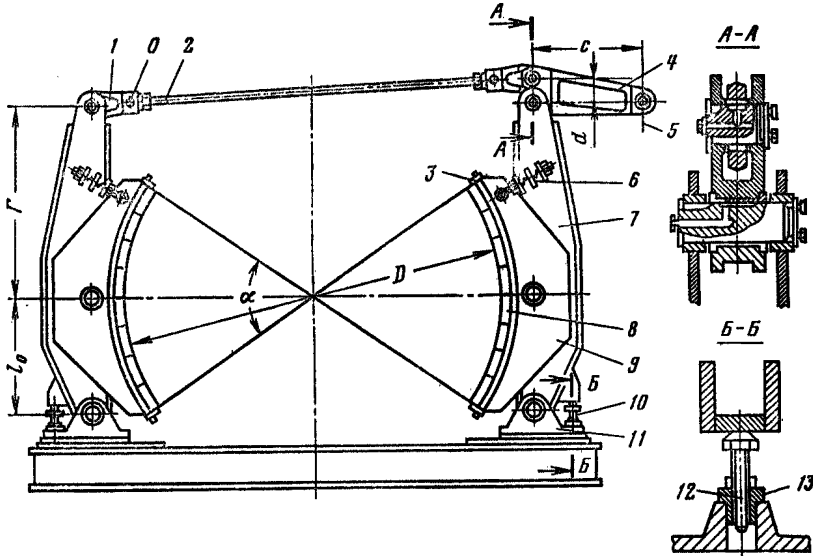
Исполнительный орган тормоза подъемных машин с пружинным приводом: 1 — головка шарнира; 2 — горизонтальная тяга; 3 — упор; 4 — угловой рычаг; 5 — ось тяги; 6 — пружинное звено; 7 — тормозная балка; 8 — фрикционные накладки; 9 — шарнирная балка; 10 — регулируемый упор; 11 — опора; 12 — упорный болт; 13 — втулка
